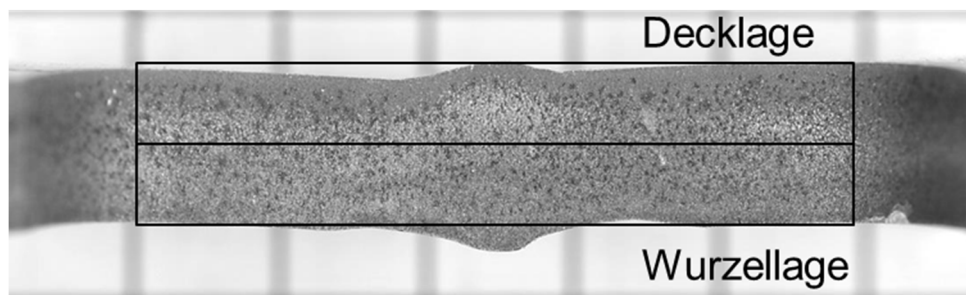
Unbearbeitete Schweißnaht mit charakteristischer Form und sichtbarem Verzug
